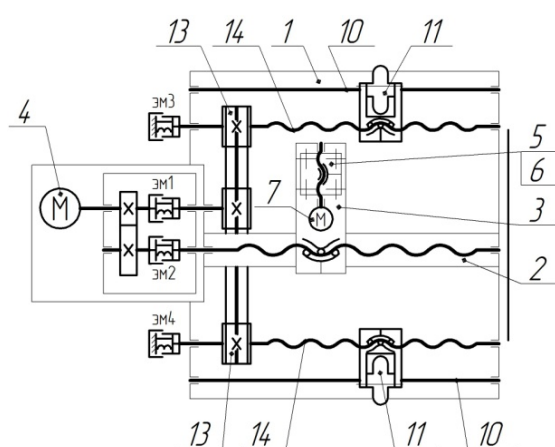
Кинематическая схема станка для обработки поверхностей крупногабаритных деталей-тел вращения
